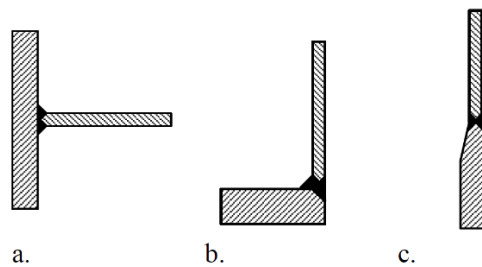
Detalhes de soldadura típicos da torre tubular. a. Soldadura na moldura da porta, b. Soldadura numa flange, c. Soldadura entre dois elementos de casca com espessuras diferentes. Fonte: [48]
